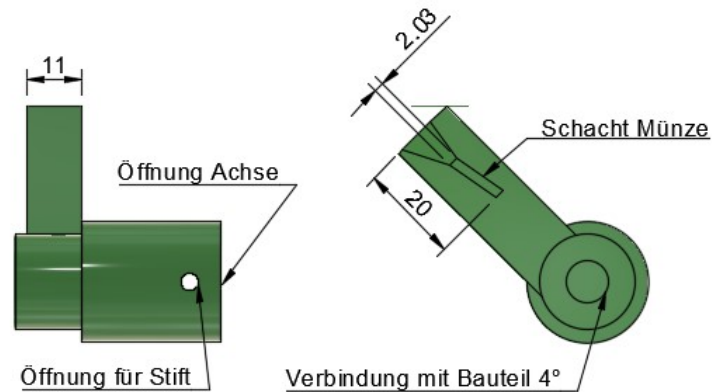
technische Zeichnung des Bauteil 3 der Baugruppe Schacht
